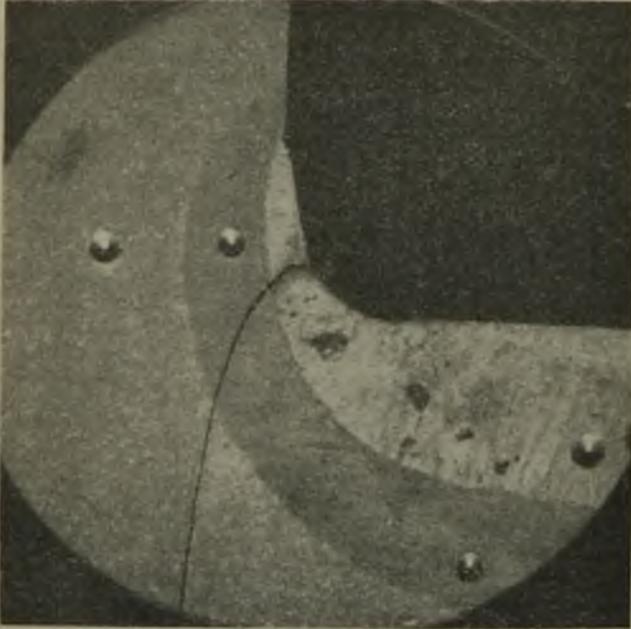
Makroschliff einer aufgeschweißten Welle.
